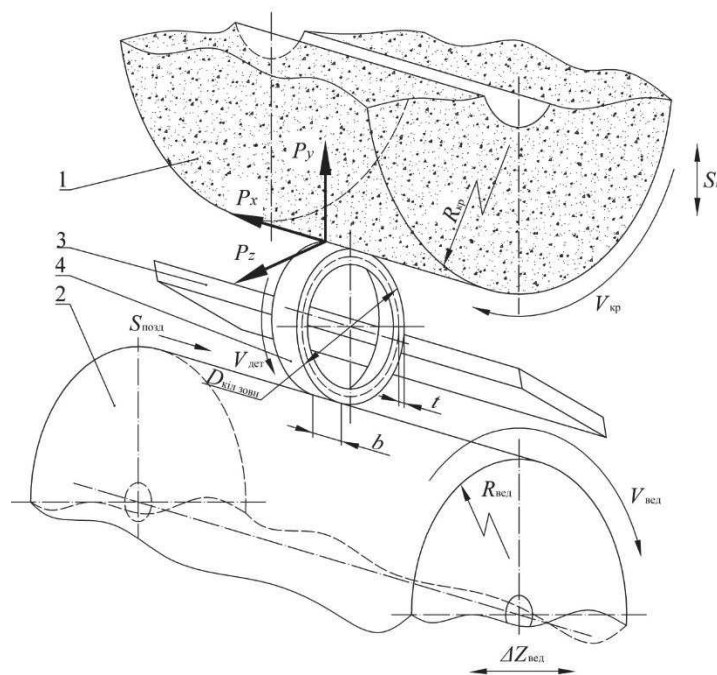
Розрахункова схема процесу шліфування: 1 – шліфувальний круг; 2 – ведучий круг; 3 – ніж опорний; 4 – заготовка
